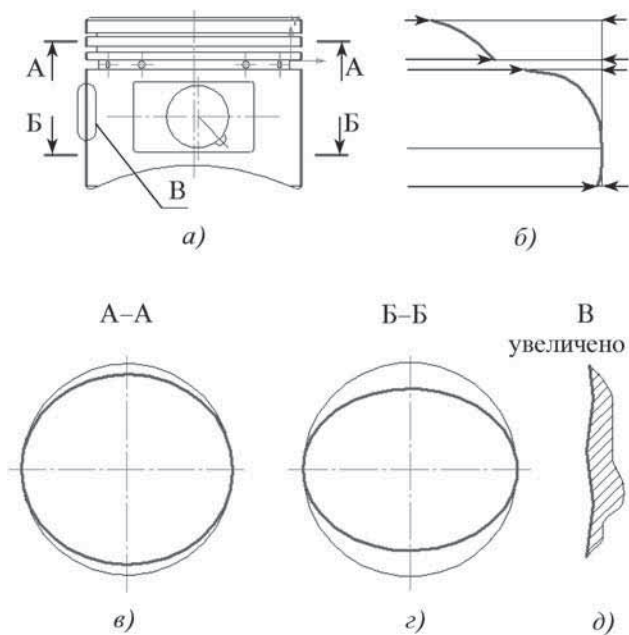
Конструктивные особенности современных поршней ДВС – их внешнего вида (а), продольного профиля (б), поперечного профиля головки поршня (в), поперечного сечения юбки (г) и микропрофиля юбки (д)
